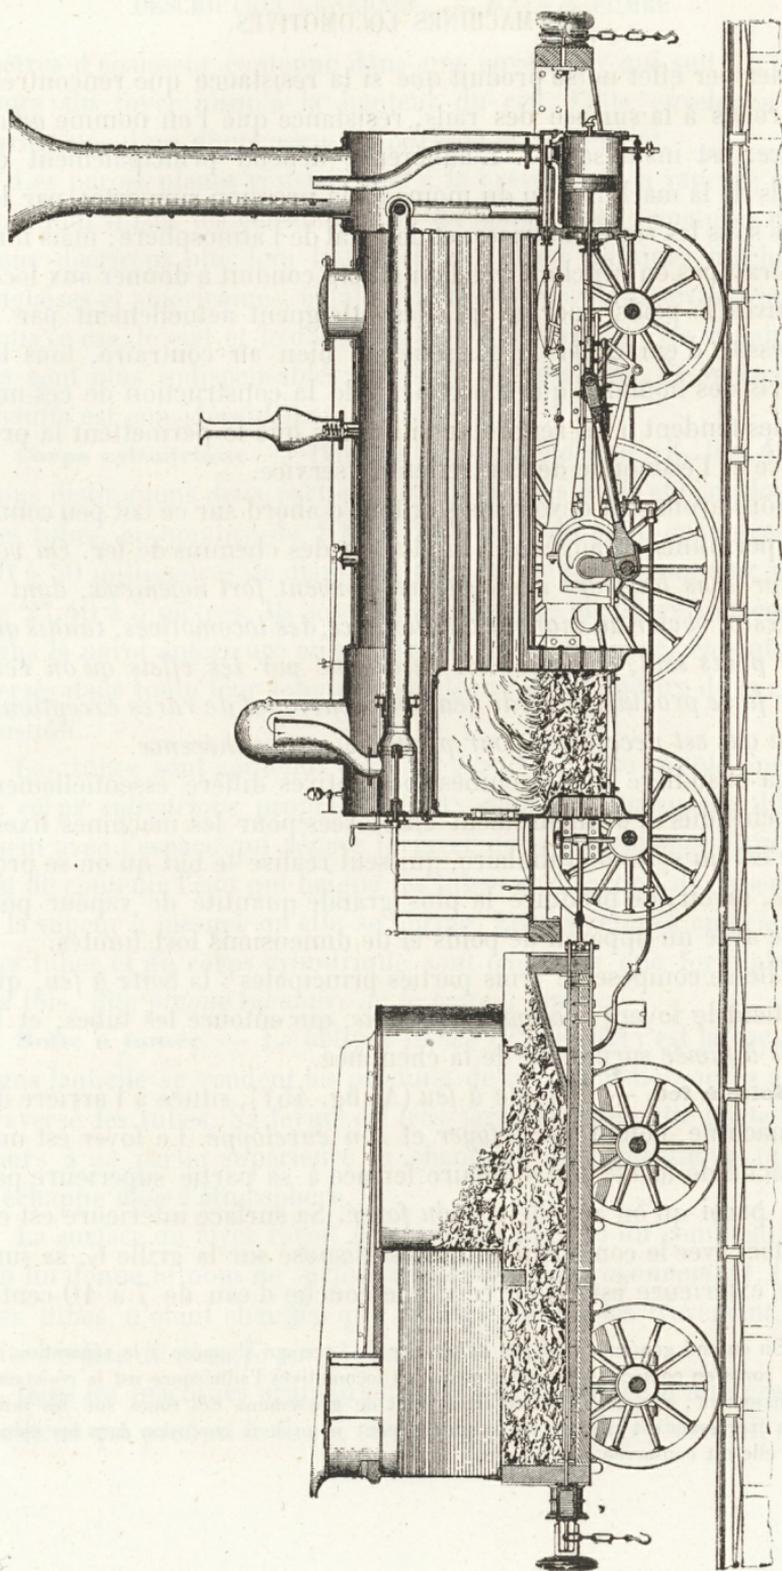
Coupe d'une machine locomotive et de son tender.
